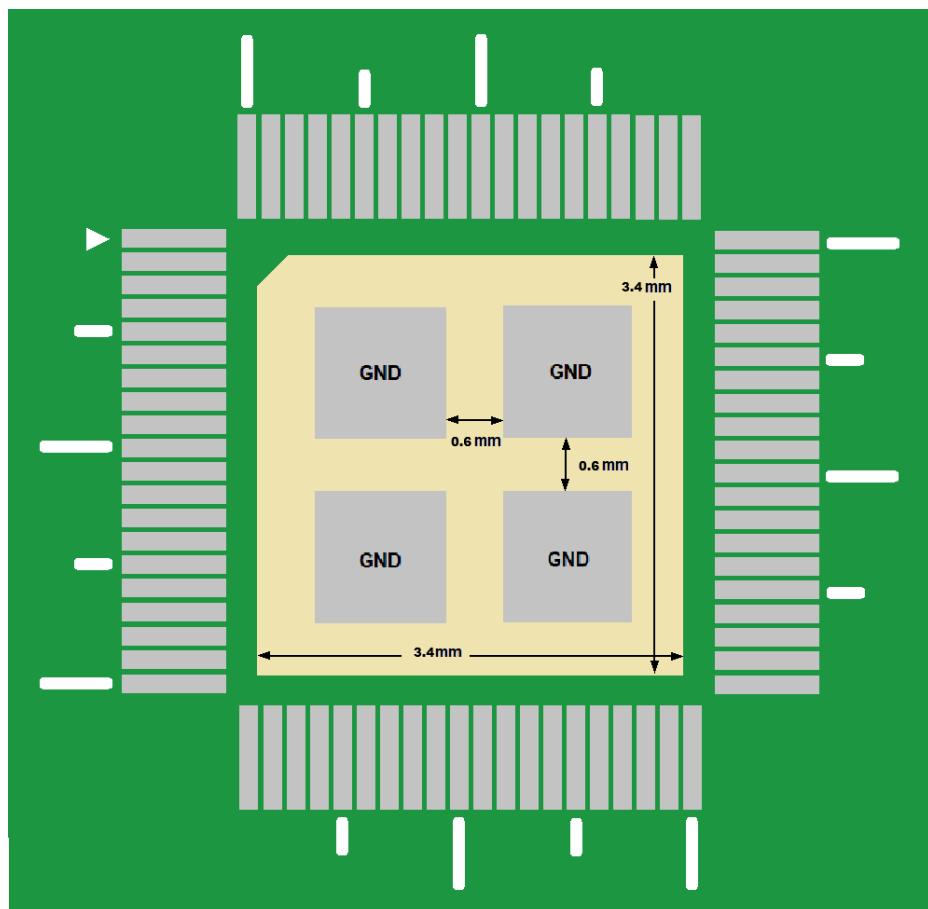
：LT165A 底部焊盘 PCB 的设计建议
